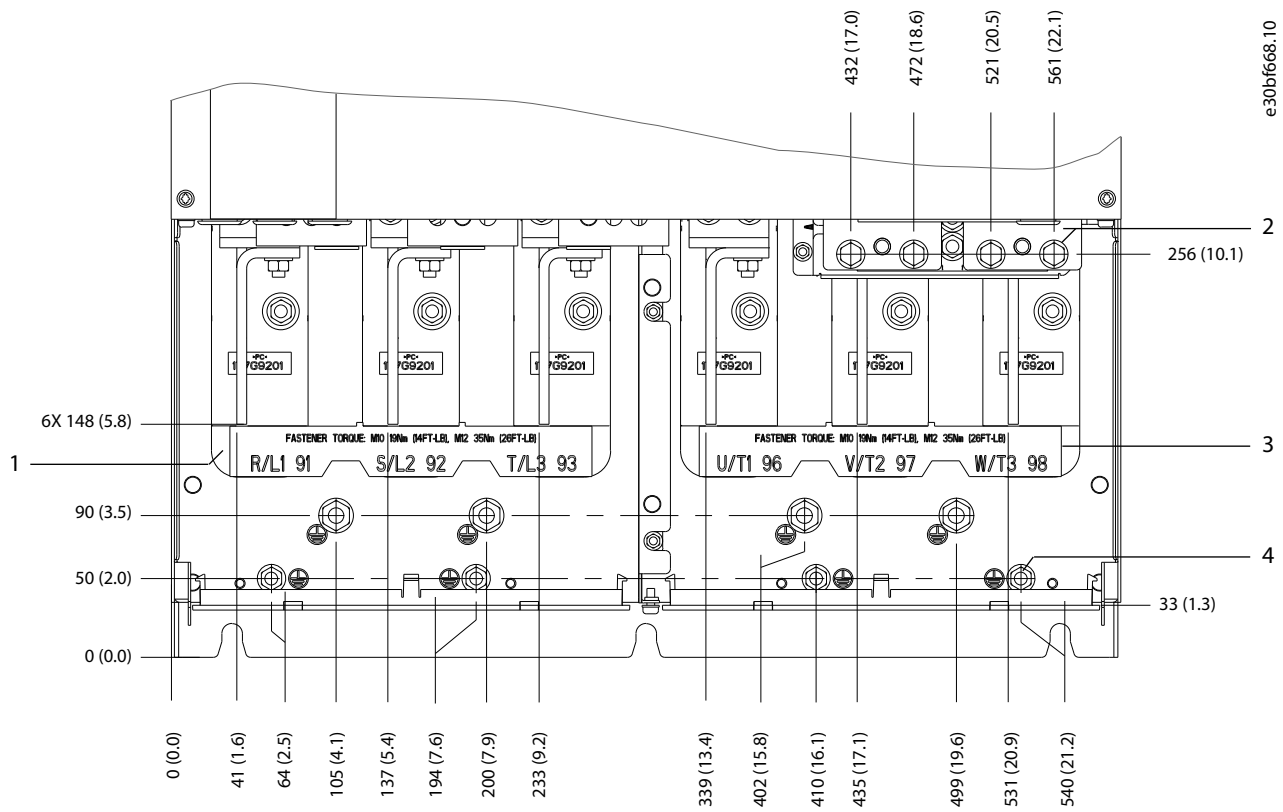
E4h-Klemmenabmessungen (Frontansicht)
